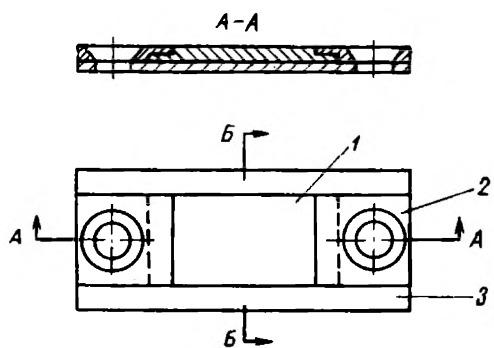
Контрольный образец для коррозии из того же металла, что и конструкция, находящаяся под наблюдением. 1 — образец весом около 200 г, обработка поверхности $\nabla\nabla$; 2 — башмак, занимающий половину образца; 3 — прокладка с пазом.
